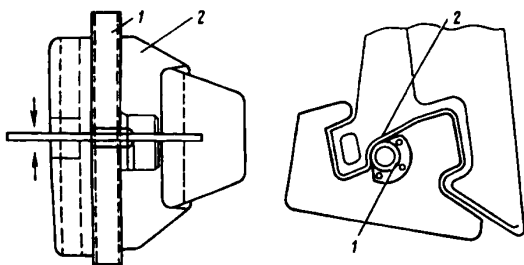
Проверка контура зацепления корпуса автосцепки проходным шаблоном 827р
